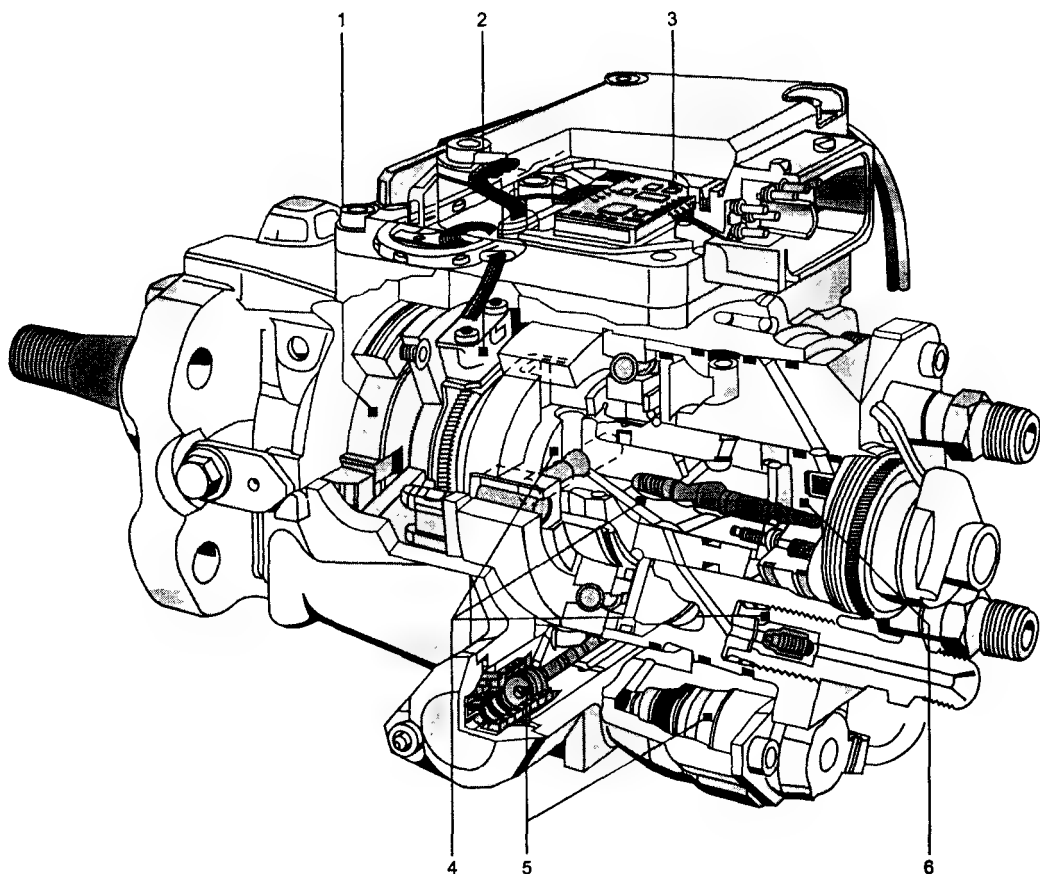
Конструкция ТНВД серии VP44: 1 — шиберный насос с клапаном регулировки давления; 2 — датчик углового положения приводного вала; 3 — электронный блок управления ТНВД; 4 — плунжеры, вал-распределитель и нагнетательный клапаны; 5 — устройство опережения впрыска и электромагнитный клапан установки момента впрыска; 6 — электромагнитный клапан высокого давления
